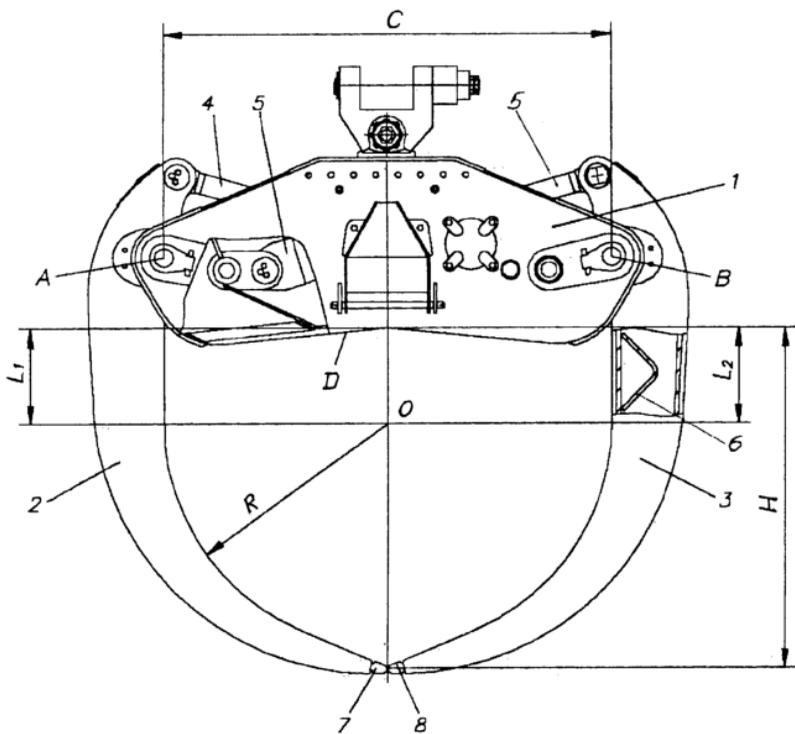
Устройство для захвата, патент РФ 2258027
